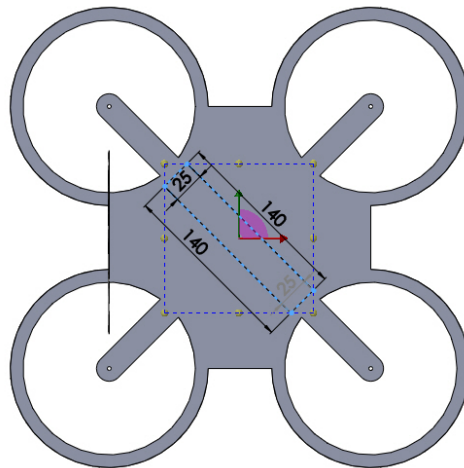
Dimensions et emplacement de la glissière.
